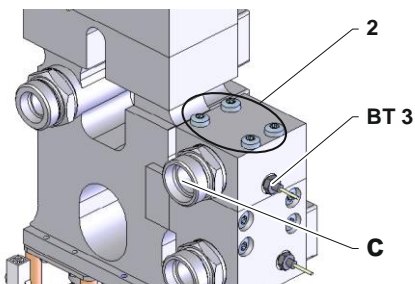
Retirer le couvercle du module de l'accumulateur
